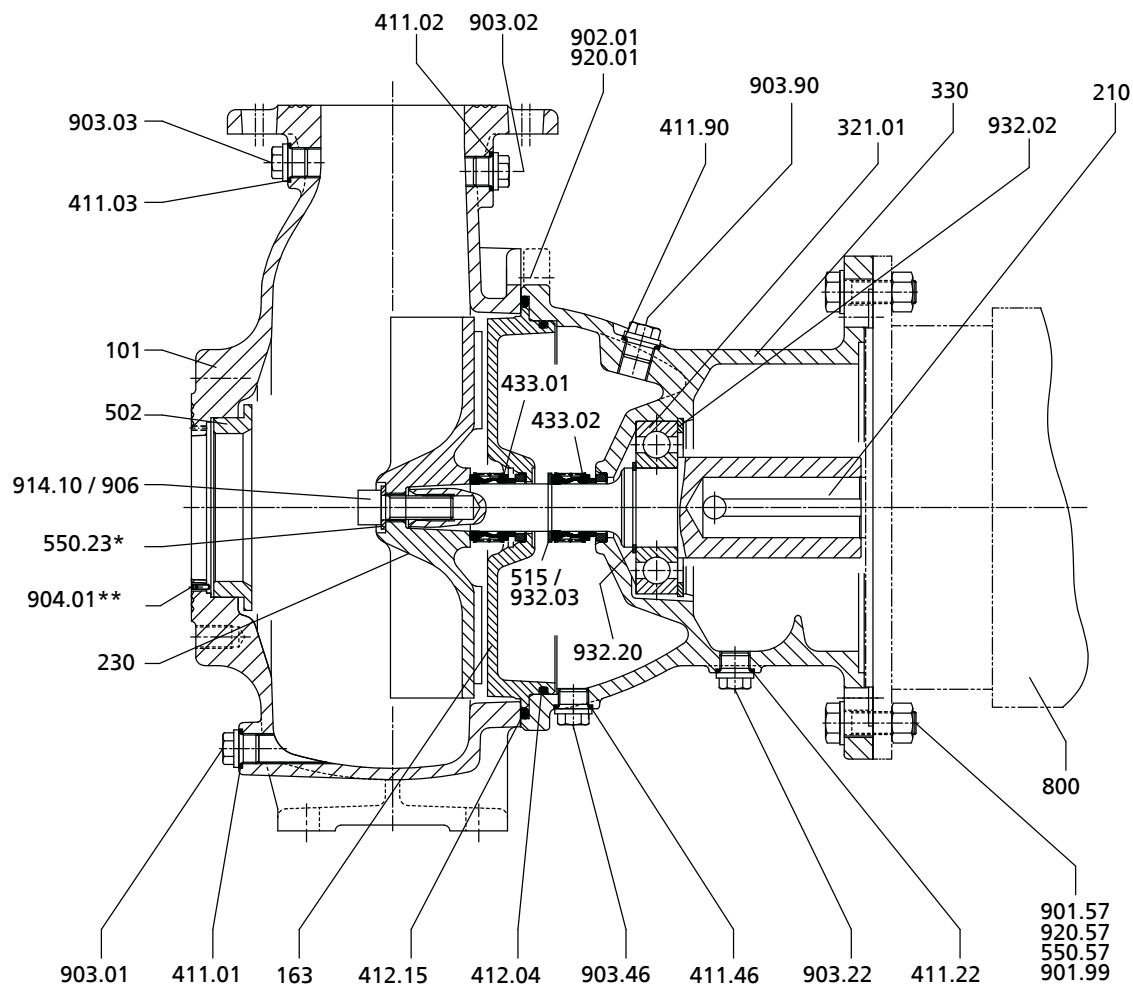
Сборочный чертеж Sewabloc; * при наличии,  только для типоразмеров 100-250, 100-251, 125-315, 150-315
